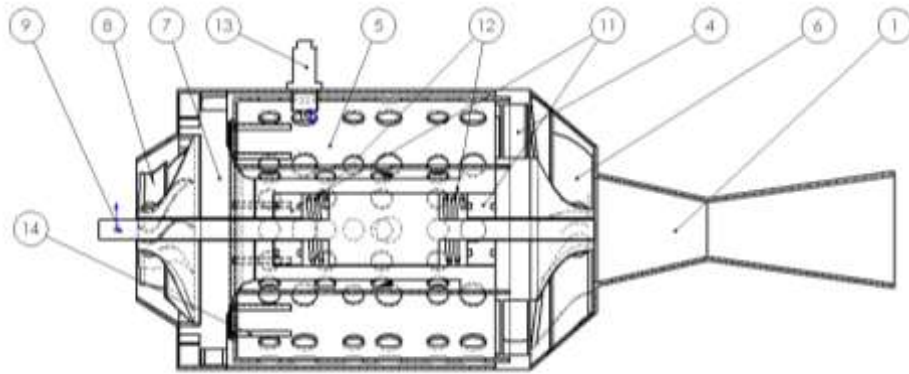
Компонировочная схема ТРД, которая включает: 1 – сопло Лавалья; 6 – турбина; 4 – статор турбины; 11 – подшипники; 12 – пружины; 5 – жаровая труба; 13 – свеча зажигания; 7 – распределитель потока; 8 – крыльчатка; 9 – вал; 14 – форсунки подачи топлива.
